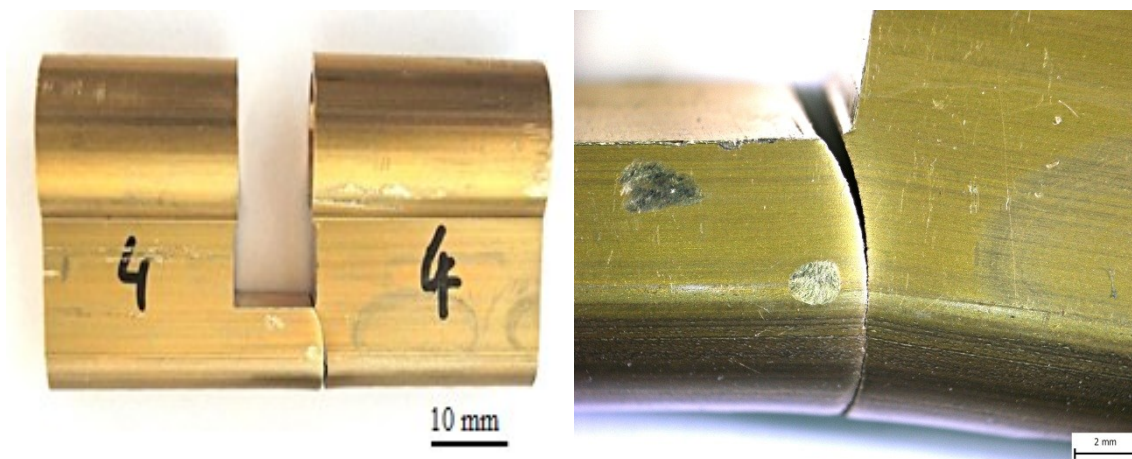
Prostor pro zub zámku zvětšeno 30x
